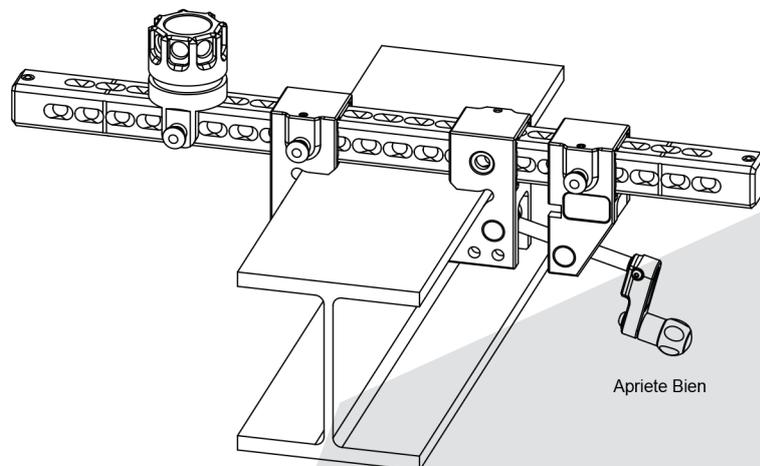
Instalación de Abrazadera Viga I Paso 4
